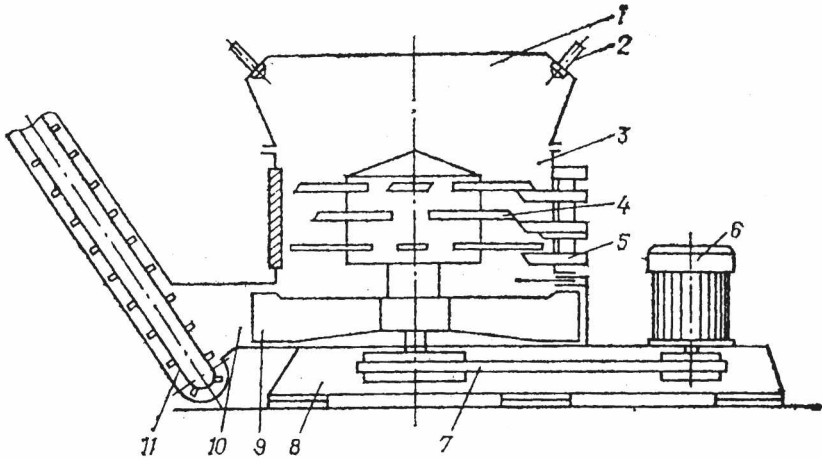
Конструктивна схема подрібнювача-змішувача ИСК-ЗА: 1 - приймальна камера; 2 - форсунка; 3 - робоча камера; 4 - ротор з ножами; 5 -нерухомі ножі (протирізи); 6 - електродвигун; 7 - клинопасова передача; 8 - рама; 9 - кидалка; 10 - розвантажувальна камера; 11 -транспортер
